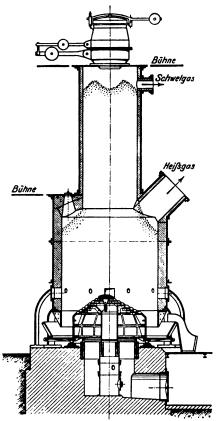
Drehrost-Gaserzeuger mit Schwelaufbau.
